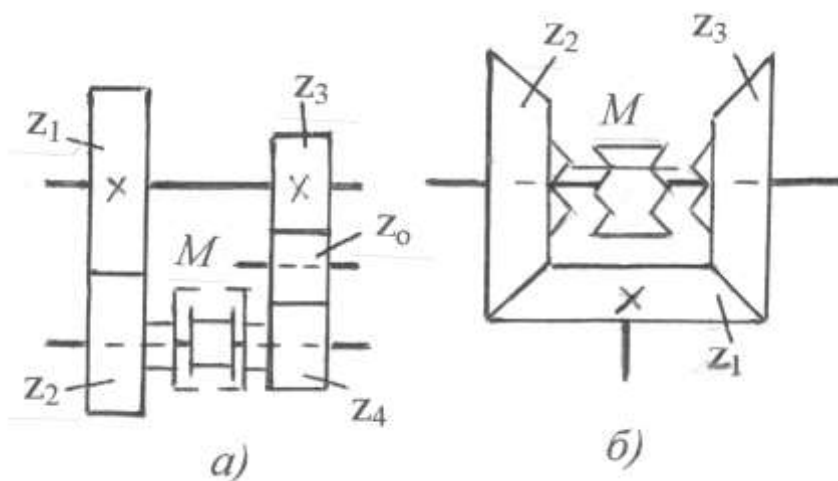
Реверсивні механізми металорізальних верстатів
